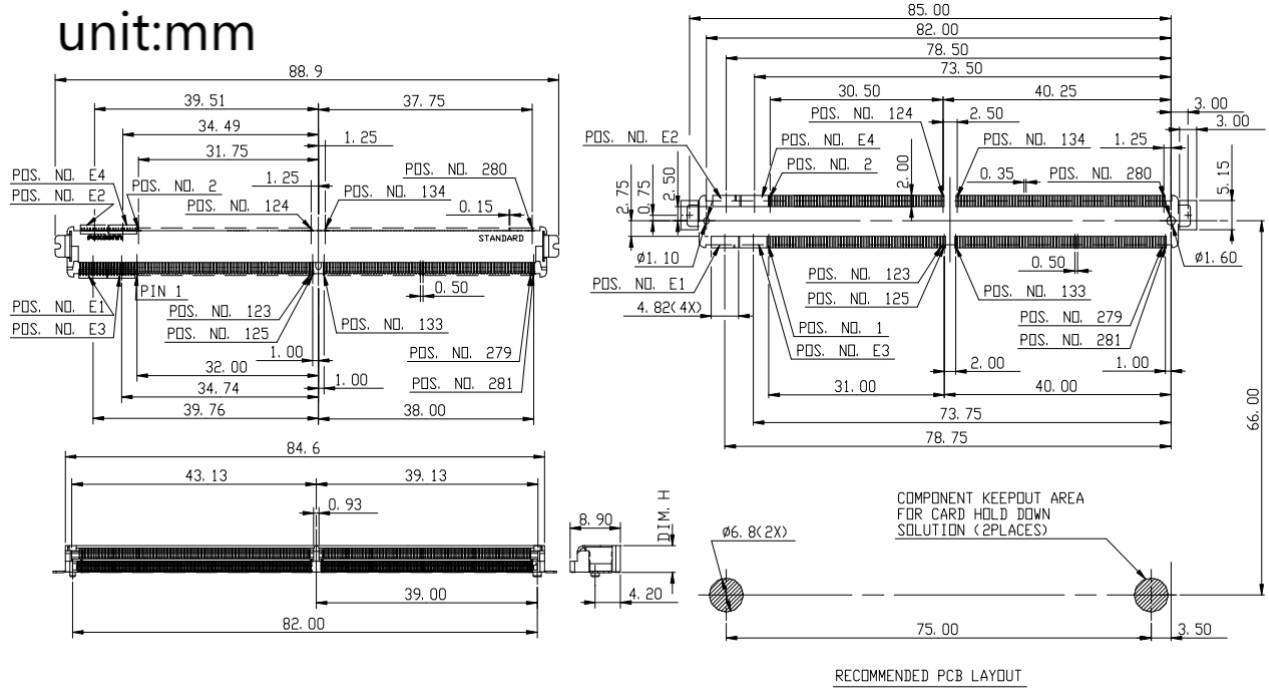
MYC-J1028X 核心板插座 PCB 封装
